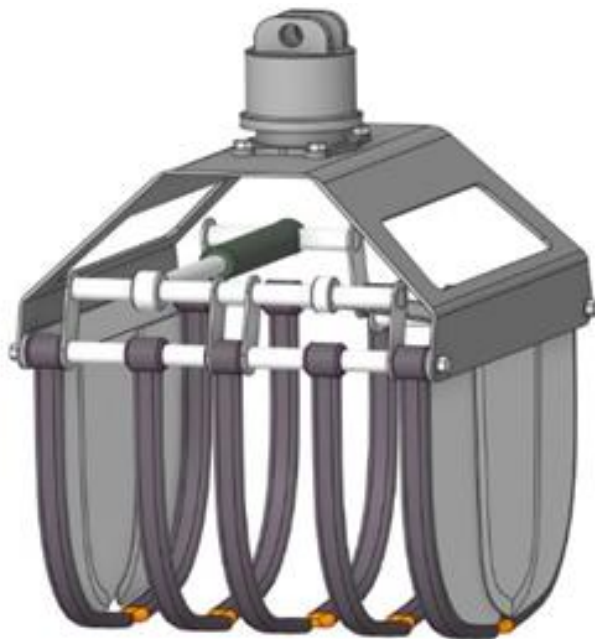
Устройство для выемки волокнистого материала с боковыми режущими парами (составлено автором)
